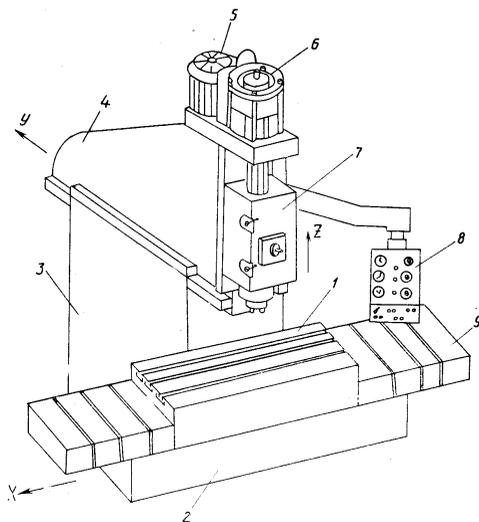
Вертикально-фрезерный станок с поперечным ползуном:
